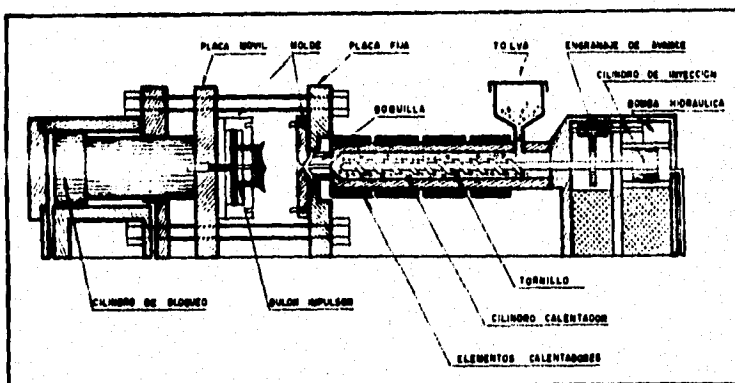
, Máquina de moldeo por inyección tipo tornillo.
